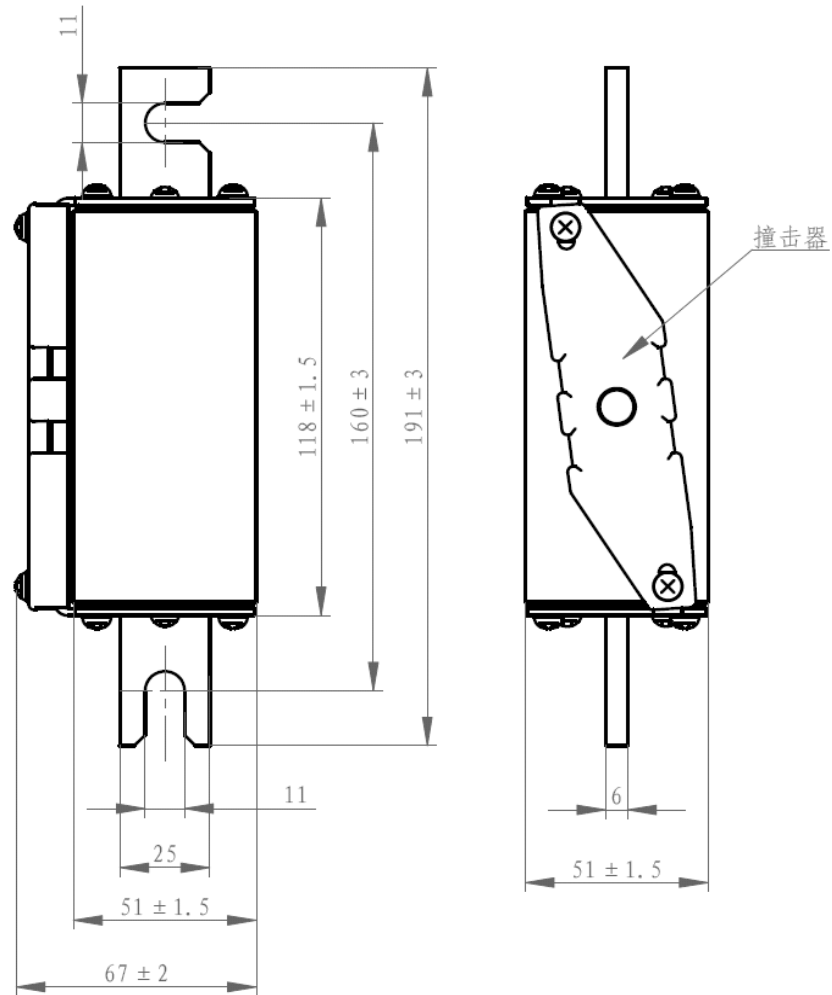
STFG10-1000/400/C1挂钩型螺栓连接的外形尺寸和安装尺寸
